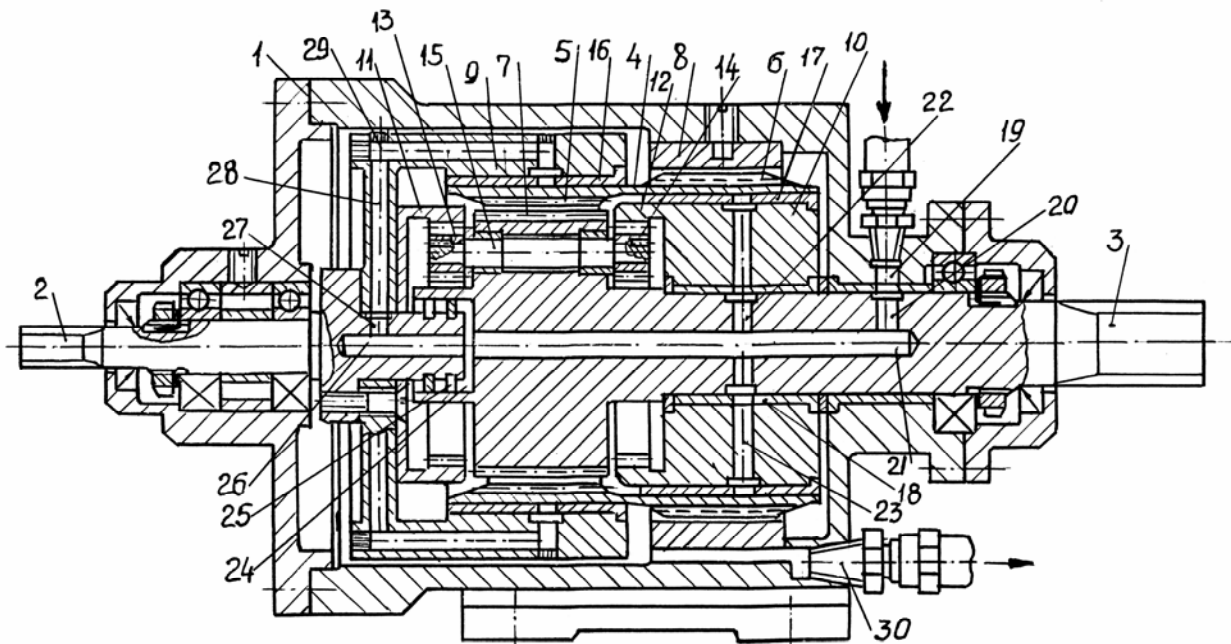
Сдвоенная волновая зубчатая передача для главного редуктора вертолета
